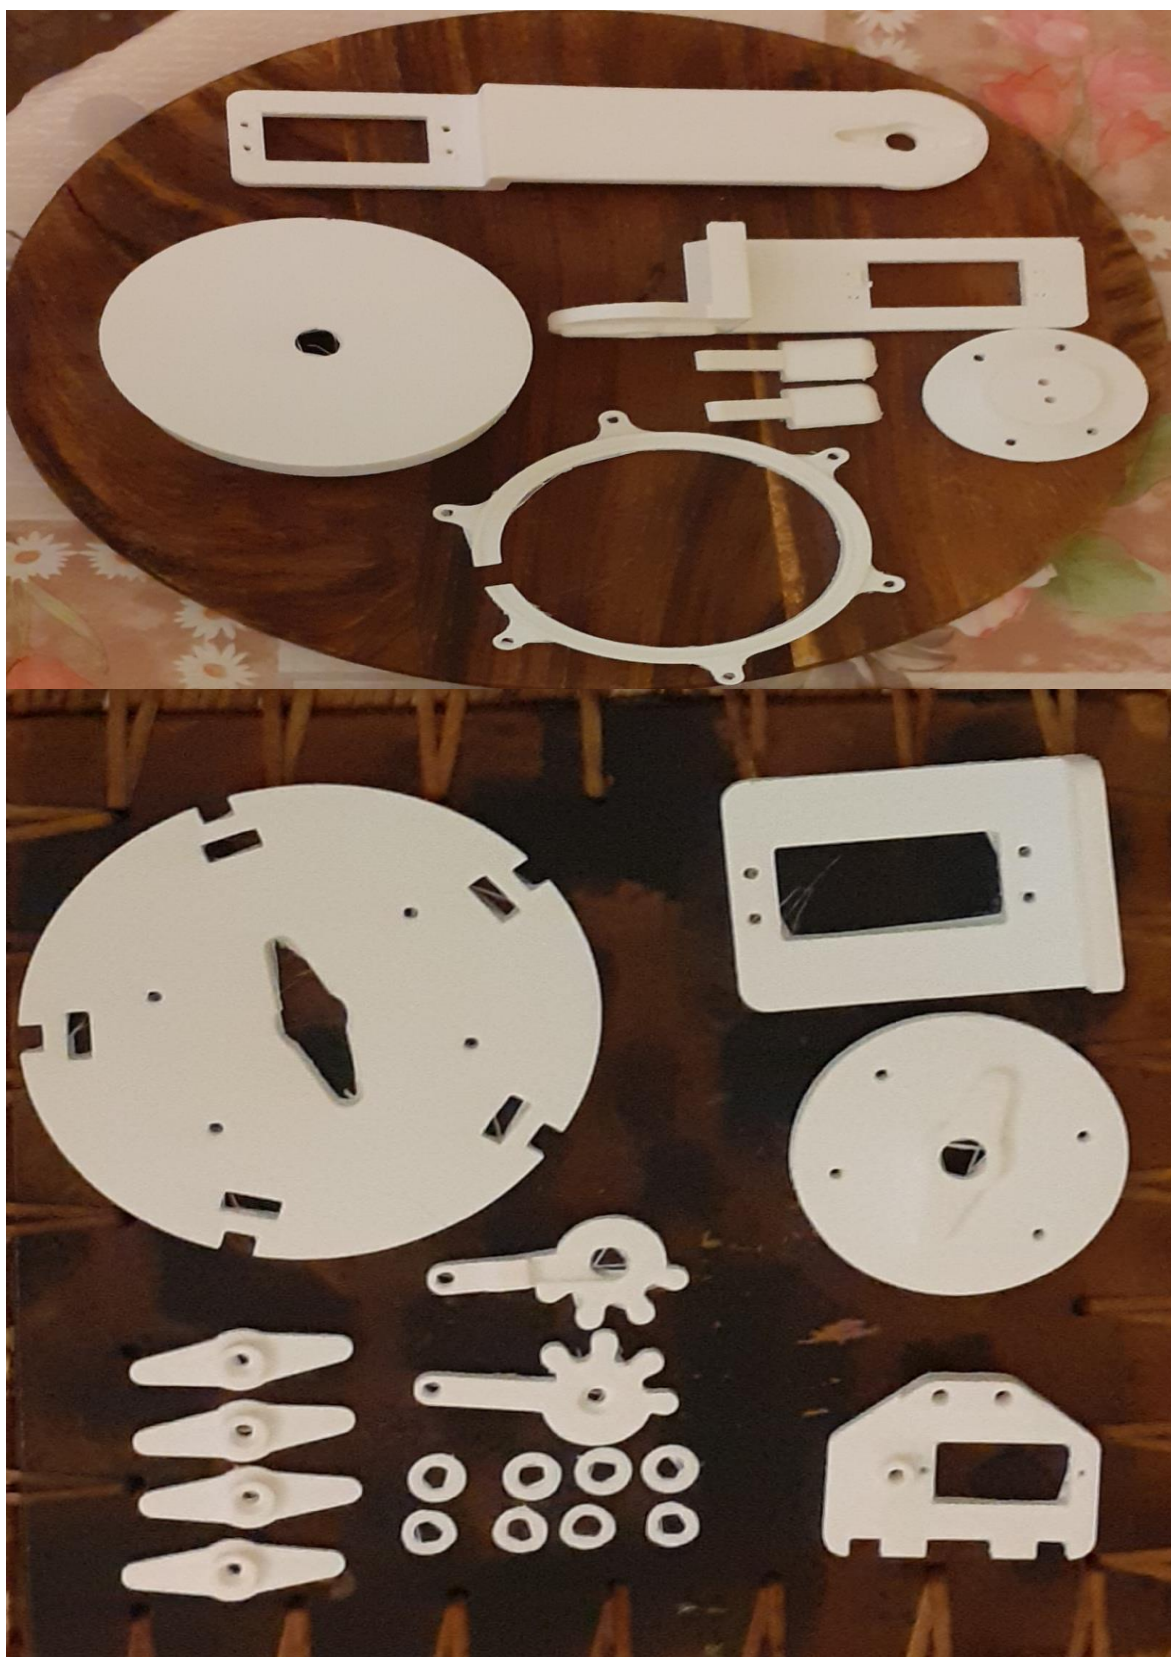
Μοχλός μετάδοσης κίνησης από fast printing
